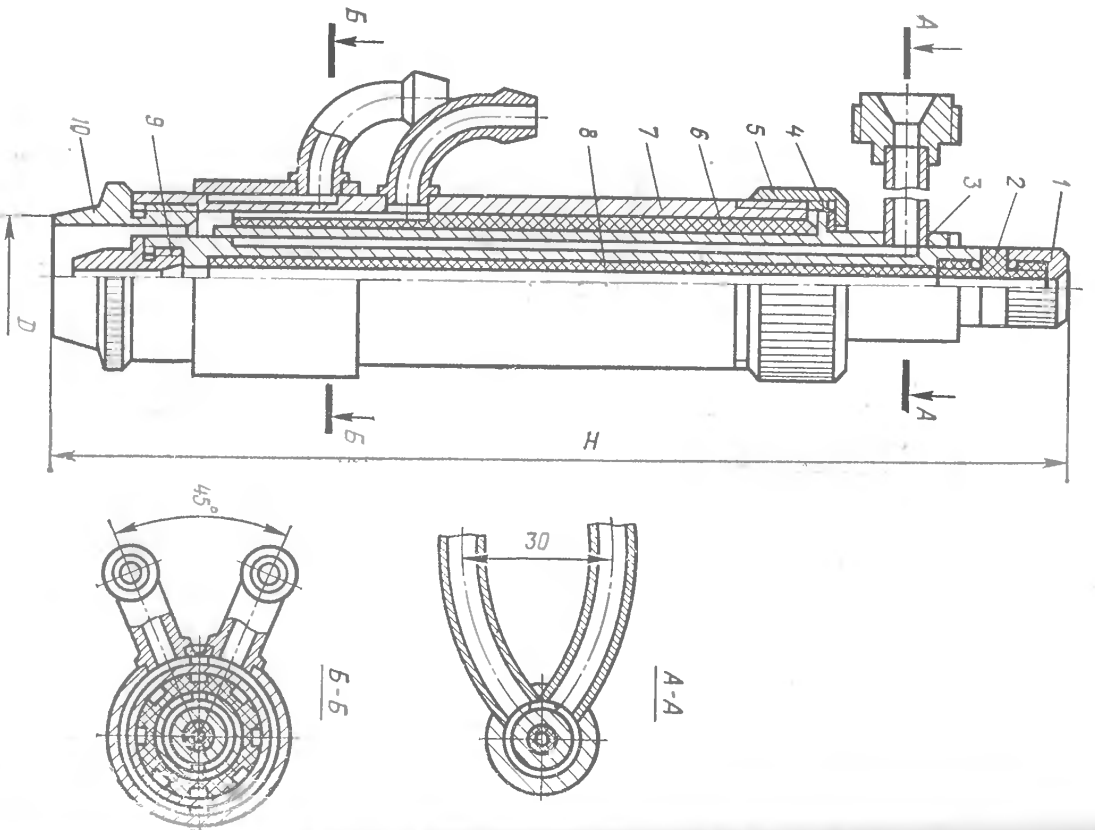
Сварочная горелка ПТА-315 с естественным (воздушным) охлаждением:
